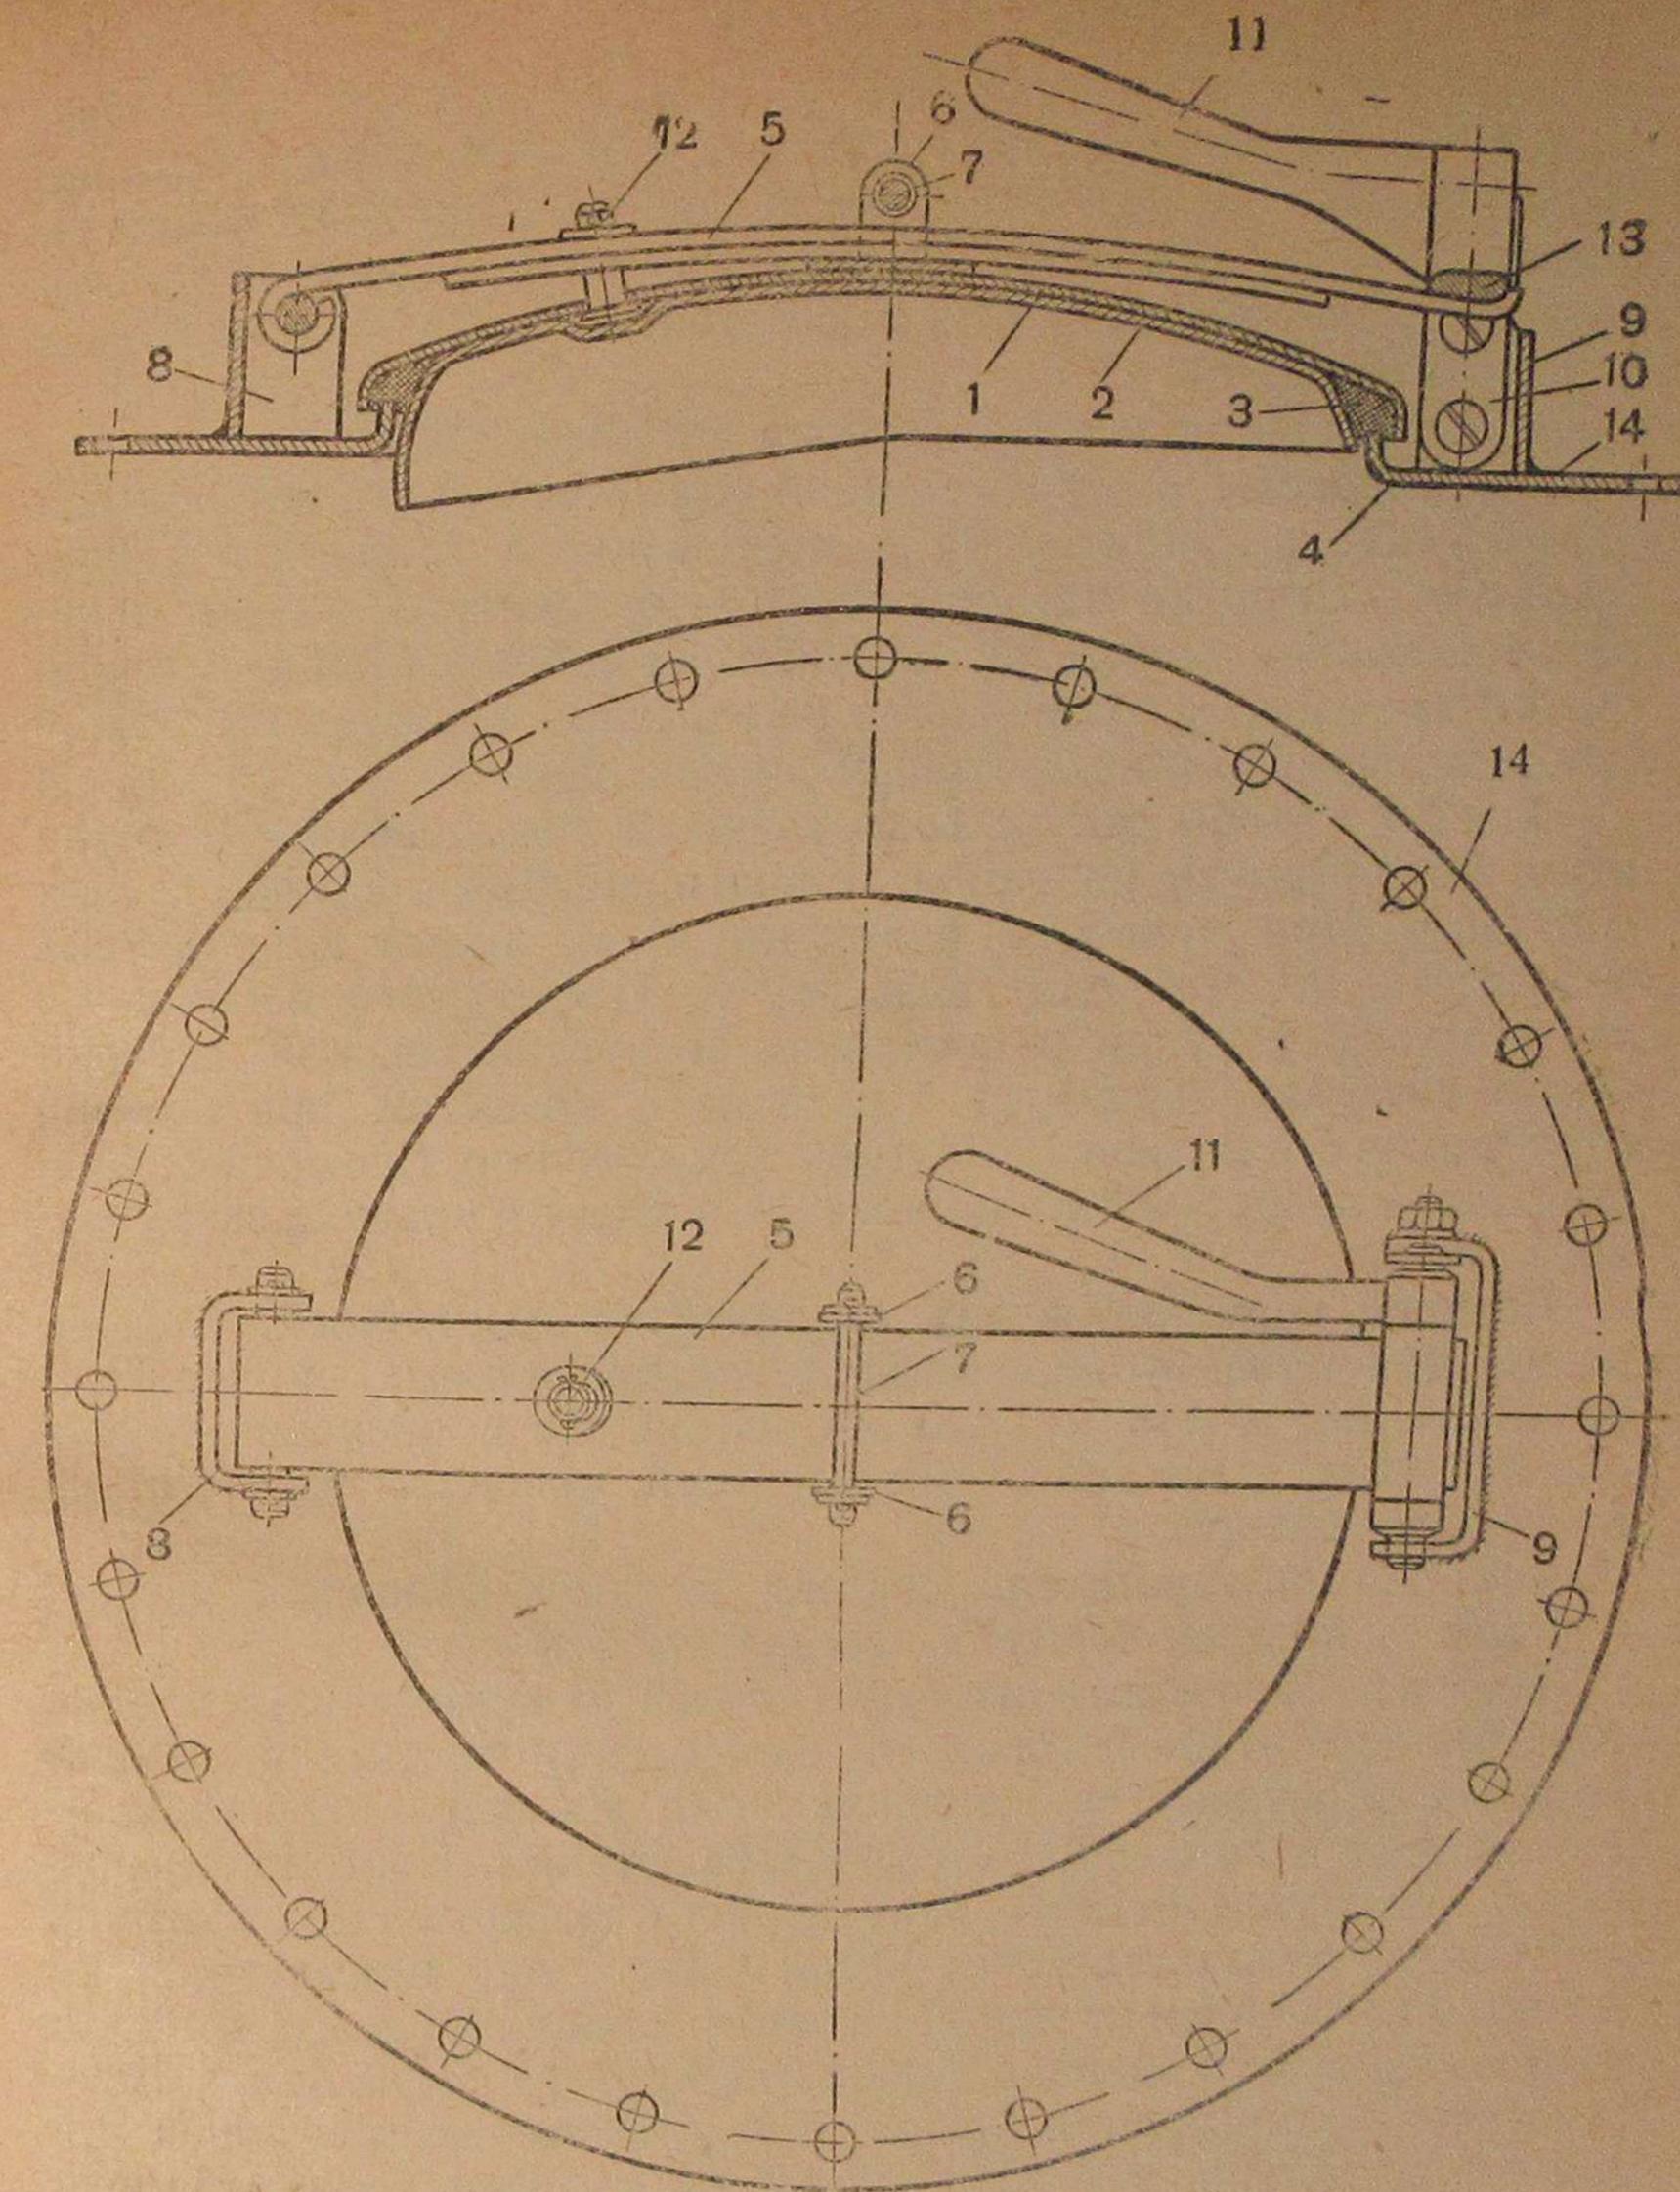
Крышка загрузочного люка газогенератора НАТИ Г-14
